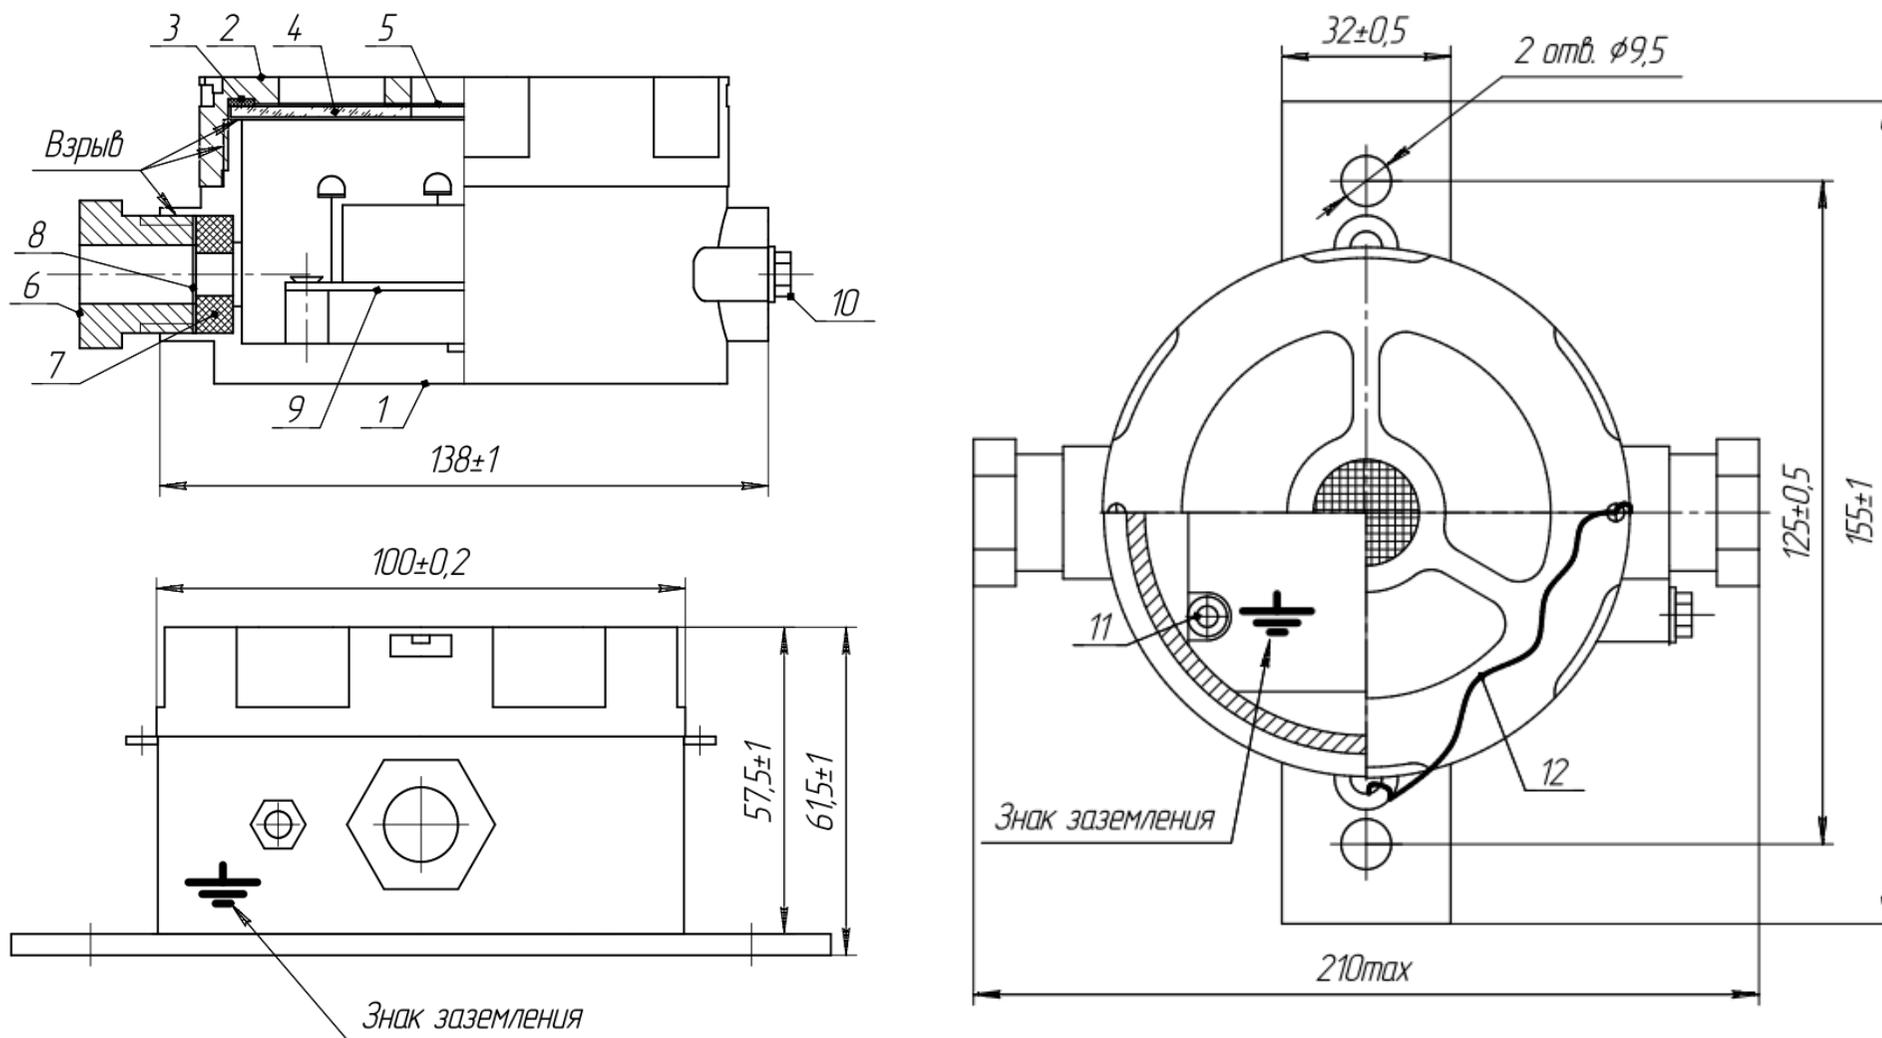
Конструкция светозвукового оповещателя Орбита МК С3 А (корпус из алюминиевого сплава).
